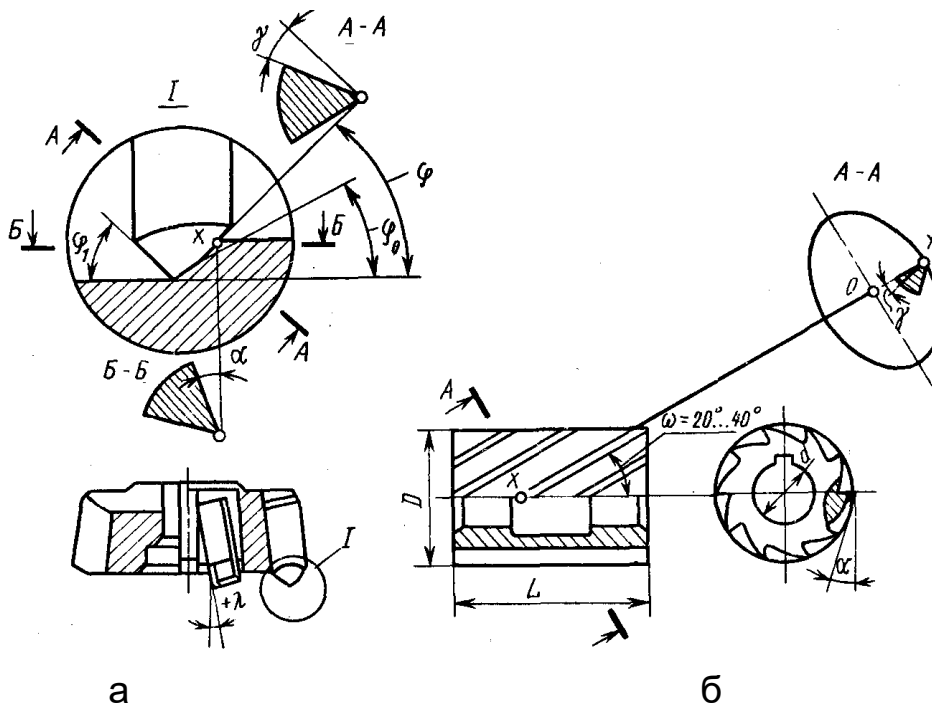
Геометрия торцовой (а) и цилиндрической (б) фрез
